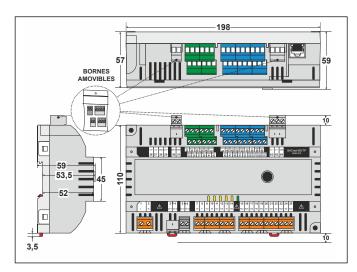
Dimensions du PCD7.LRL2 (en mm)
